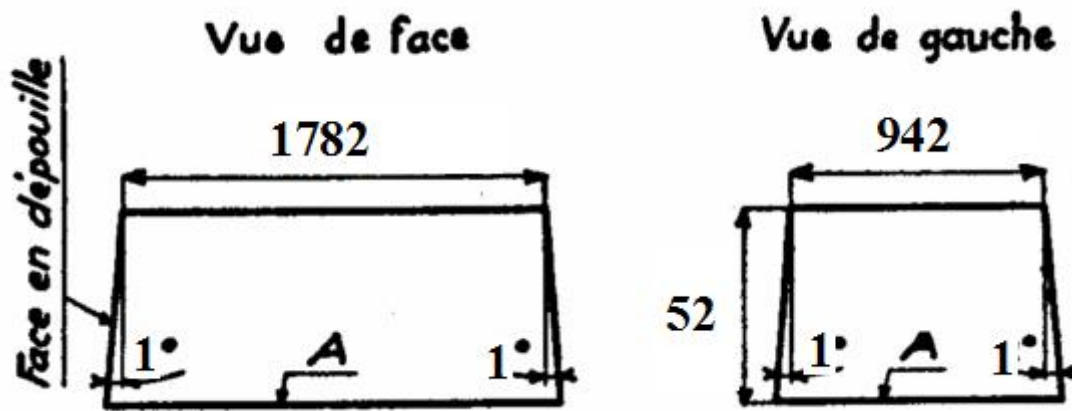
Forme et dimensions de l'ébauche brute après démoulage [18]
